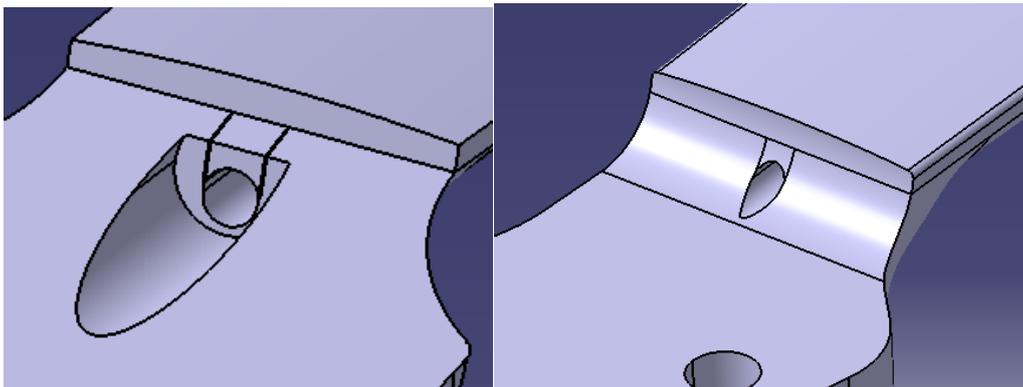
Detalles de la división del sólido en las distintas piezas que conforman el conjunto mástil (diapasón, resto del mástil y varilla que cubre la barra de refuerzo).
